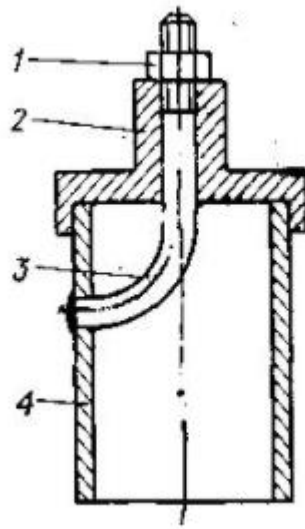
Приварка шпильки до корпусу ковпачка
